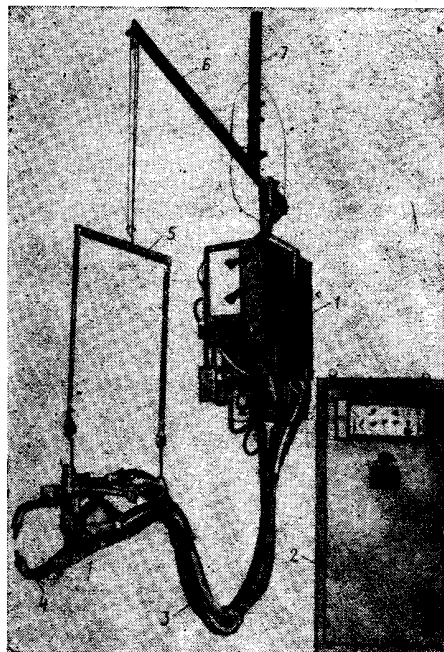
Подвесная сварочная машина МТП-806
